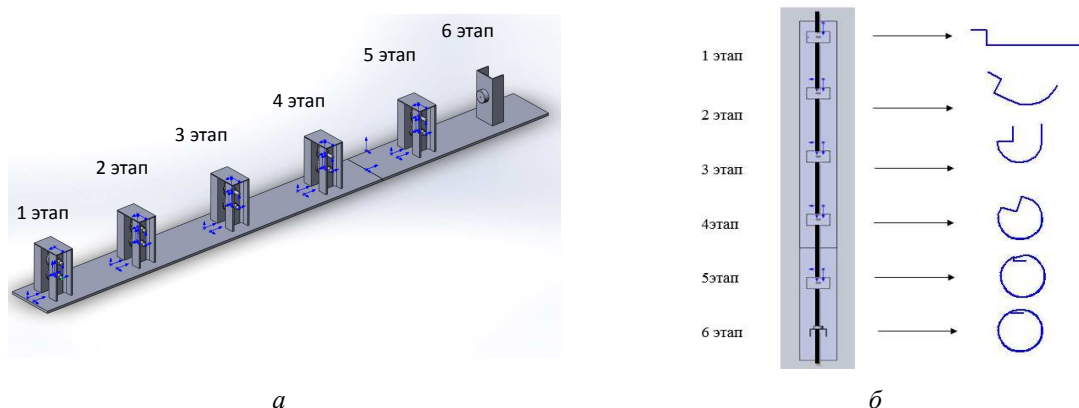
Формообразование сварочной порошковой проволоки из стальной ленты сплошного сечения:
